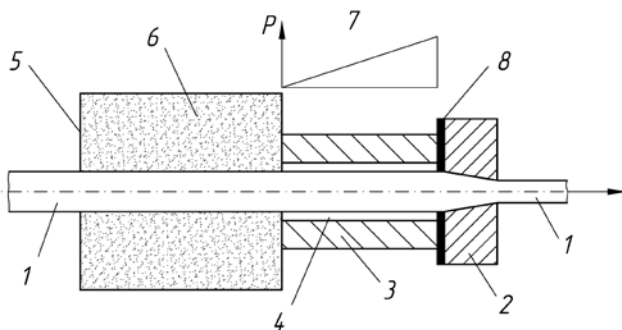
Схема волочения с гидродинамической подачей смазки:
